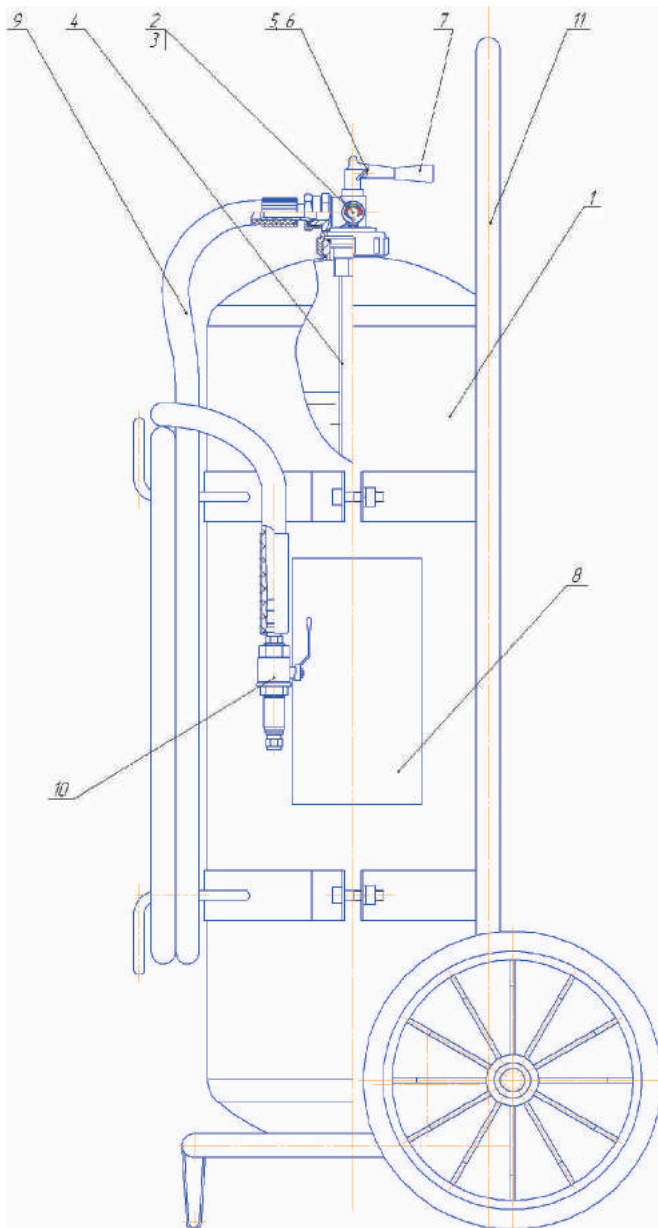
1 – корпус огнетушителя, 2 – запорно-пусковое устройство, 3 – индикатор давления, 4 – сифонная трубка, 5 - предохранительная чека, 6 - пломба, 7 – рычаг запорно-пускового устройства, 8 – этикетка, 9 – рукав высокого давления, 10 – пожарный швол с распылительным соплом, 11- тележка для перемещения огнетушителя.
